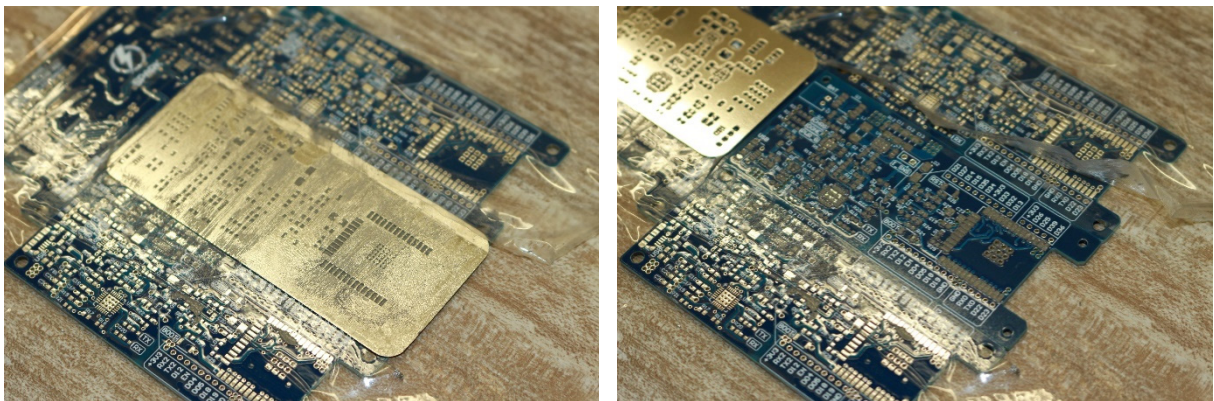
Stencil i aplicació de pasta de soldadura
